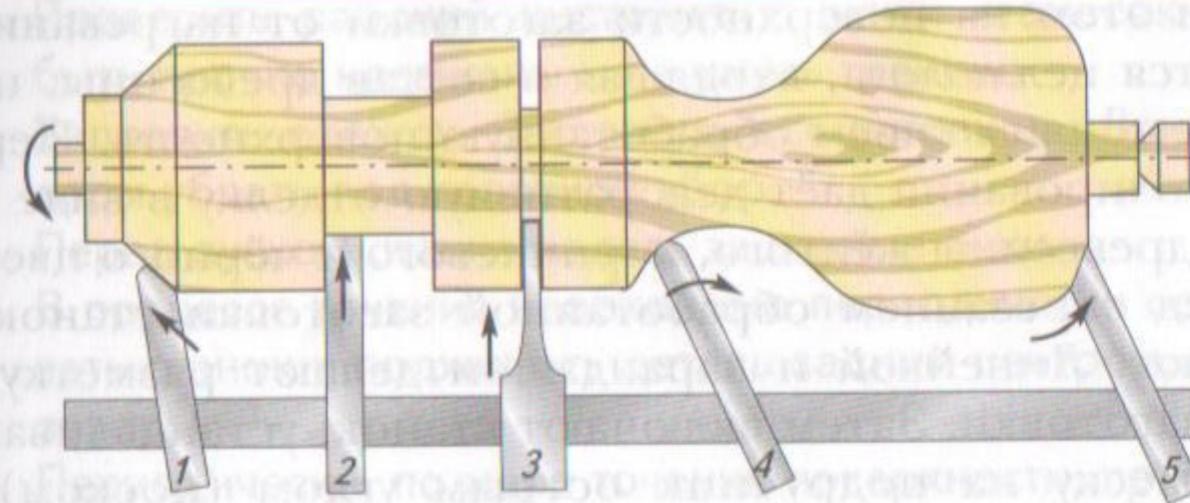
Профили поверхности детали и направления подачи стамесок:
